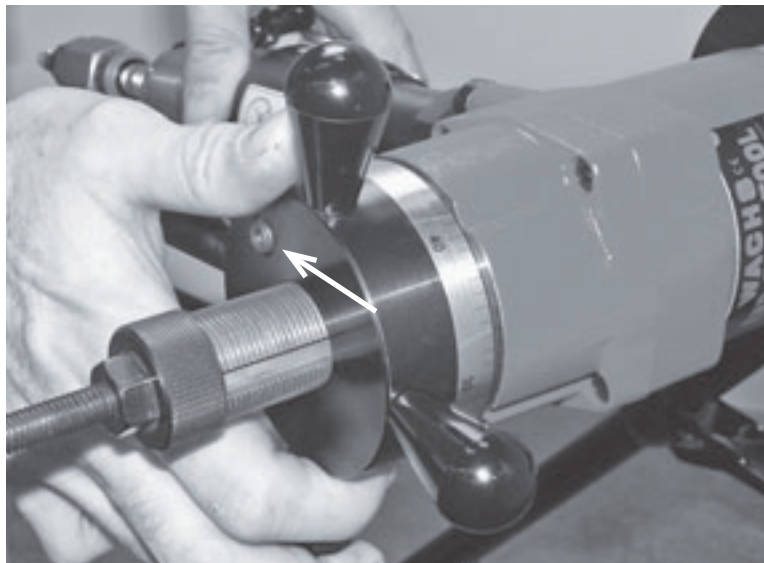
Ziehen Sie die Einstellschraube des Vorschubhebels an, damit die sich Maschine während der Flanschplanbearbeitung nicht radial bewegt.
